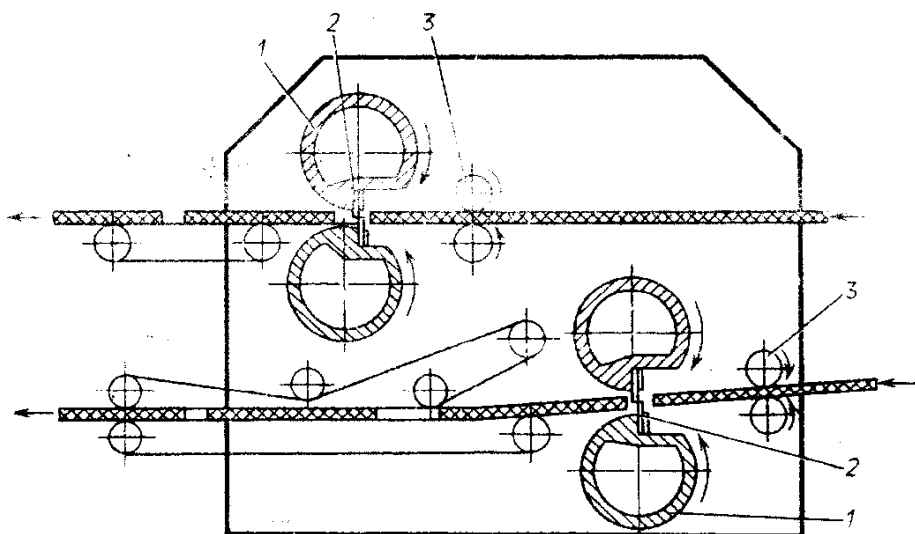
Схема двухъярусной поперечно-режательной машины:
